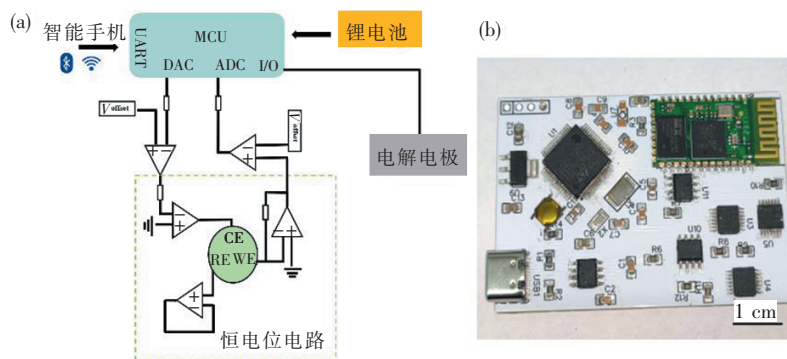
(a) 电路设计系统示意图; (b) PCB 背面实物图
